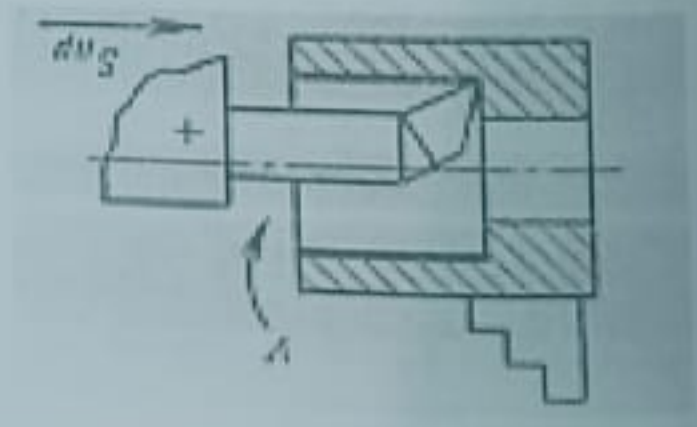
Схема обработки заготовок на токарно-винторезном станке, гидро-распашной резец.
